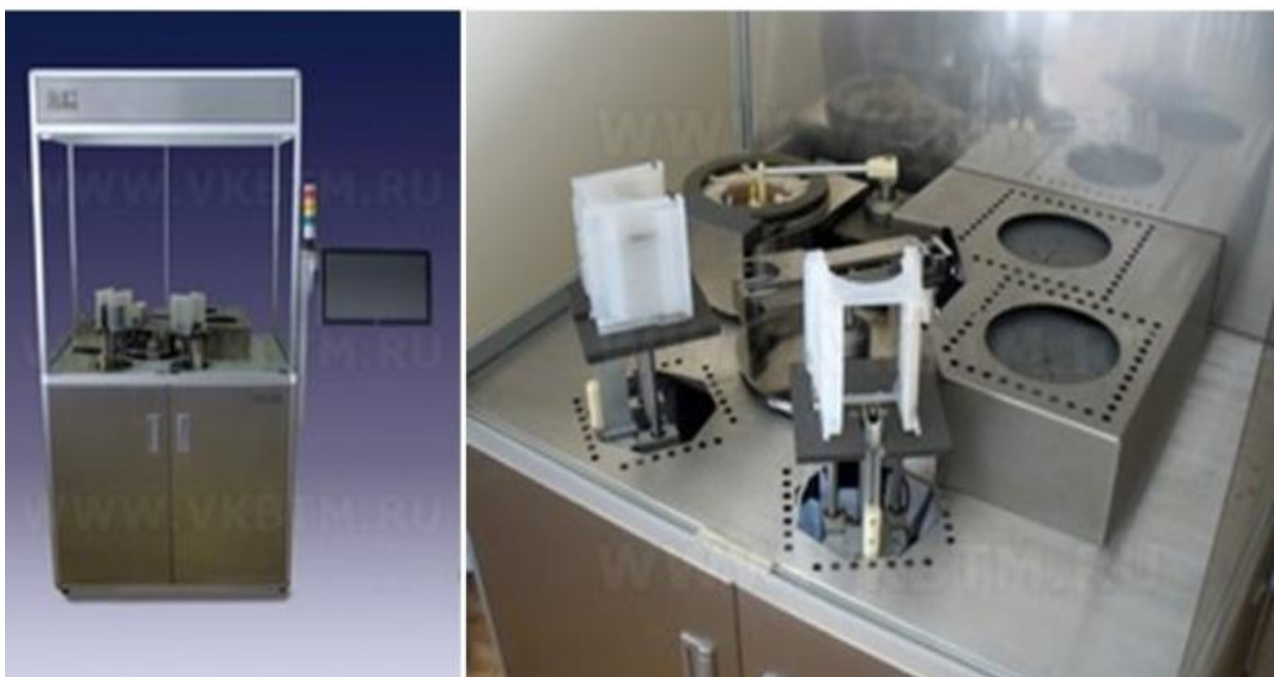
Автоматизированная установка нанесения фоторезиста
